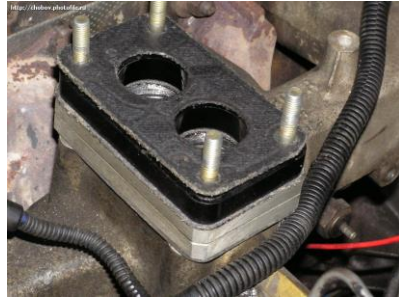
Загальний вигляд центрування прокладки вздовж стержнів шпильок карбюратора двигуна
